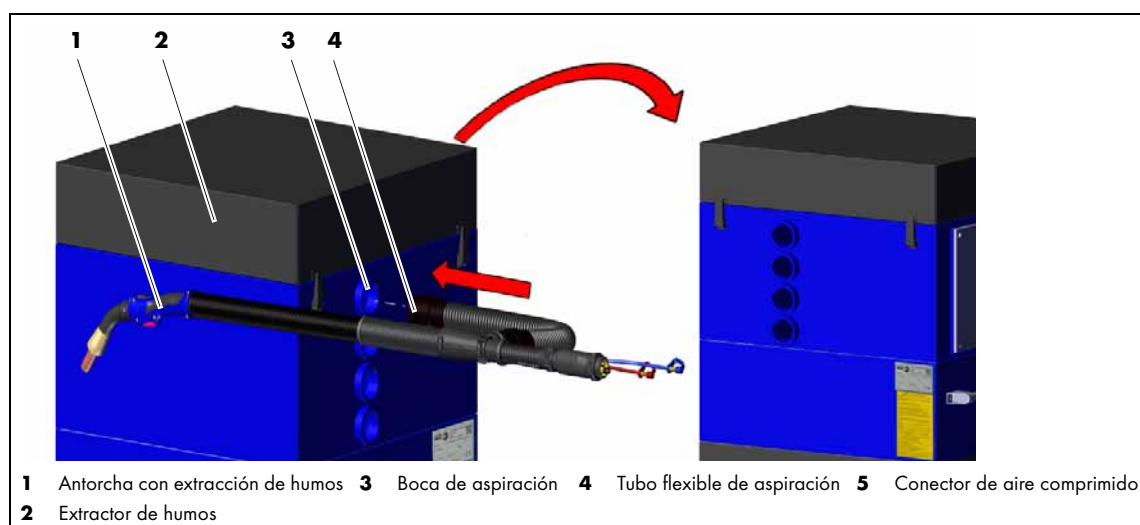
Montaje del tubo flexible de aspiración de la antorcha de soldadura
